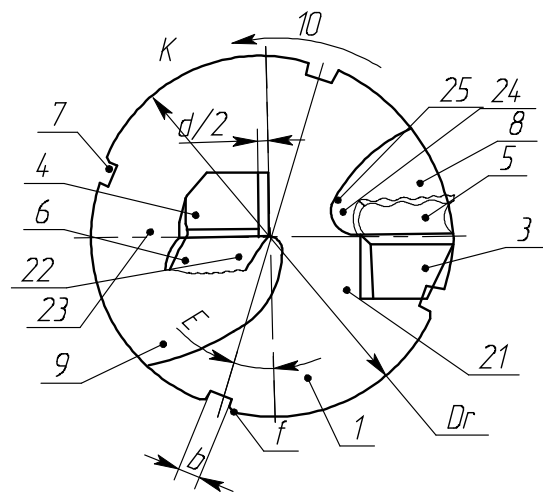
Вид на резцовую головку по стрелке K с исполнением 1 корпуса.
